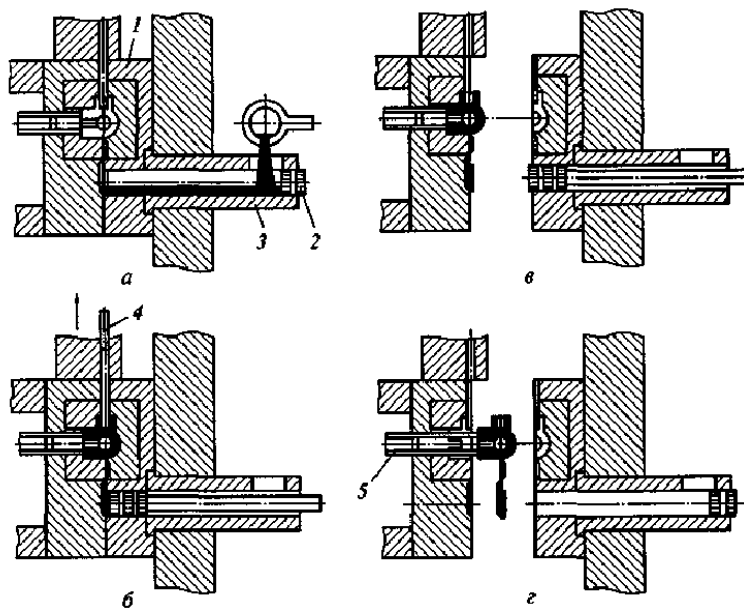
Схема технологического процесса литья под давлением на машине с холодной камерой прессования: а — подача расплава в камеру прессования; б —
